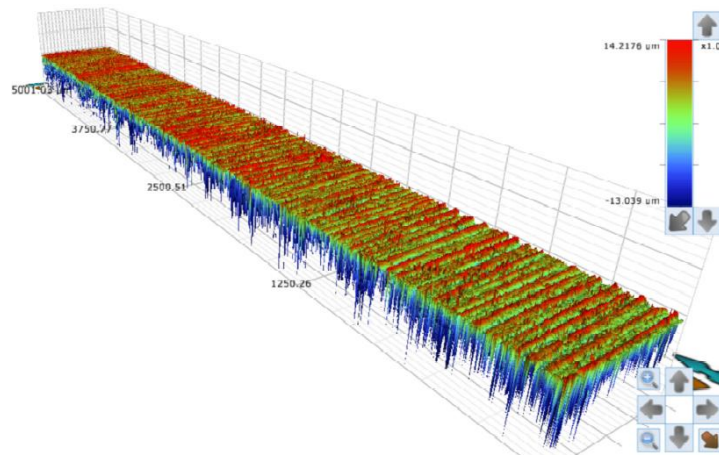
Vista 3D da superfície de medição de rugosidade da serra Fabricante 3.
